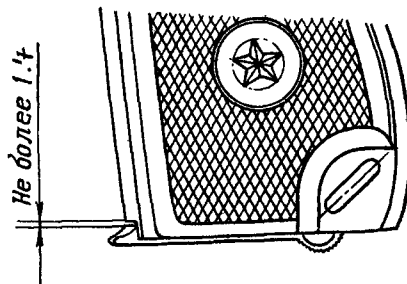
Зазор между основанием рукоятки и крышкой магазина
